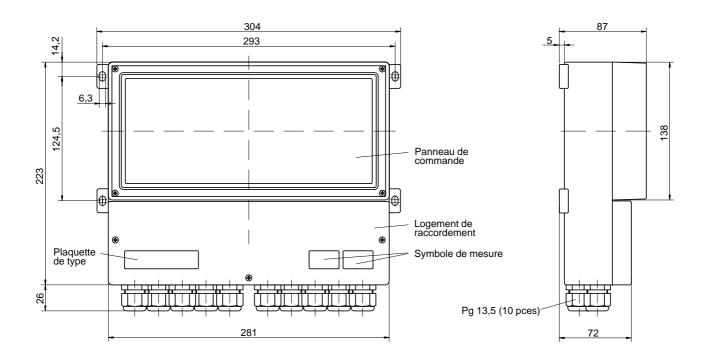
Dessin d'encombrement du Transmetteur de pH 2500
